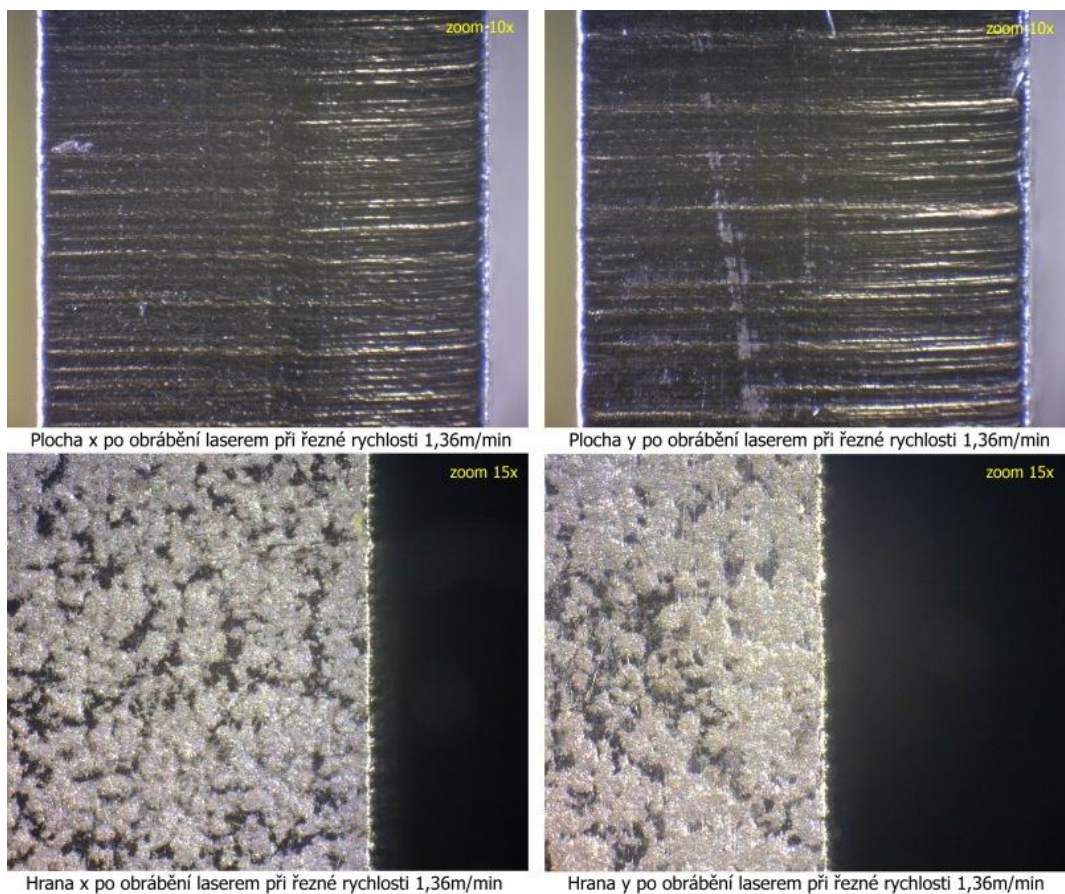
Snímky z mikroskopu vzorku 3 obráběného laserem - materiál 17 349
